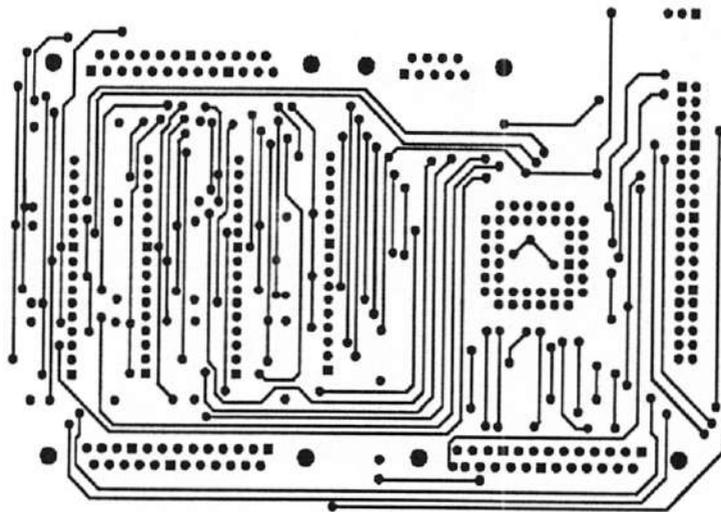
Anverso del Layout del PCB (lado de componentes).
